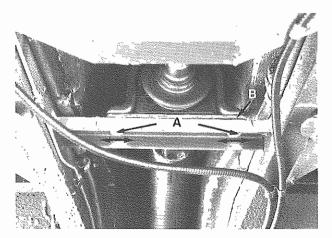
A - Viti fissaggio supporto albero al telaio Screws fixing shaft support to frame
